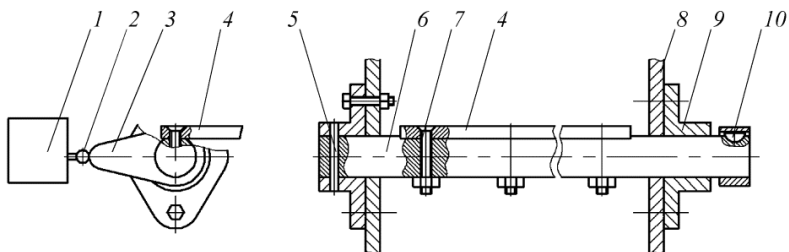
Схема конструкции защитного устройства противорежущей пластины:
